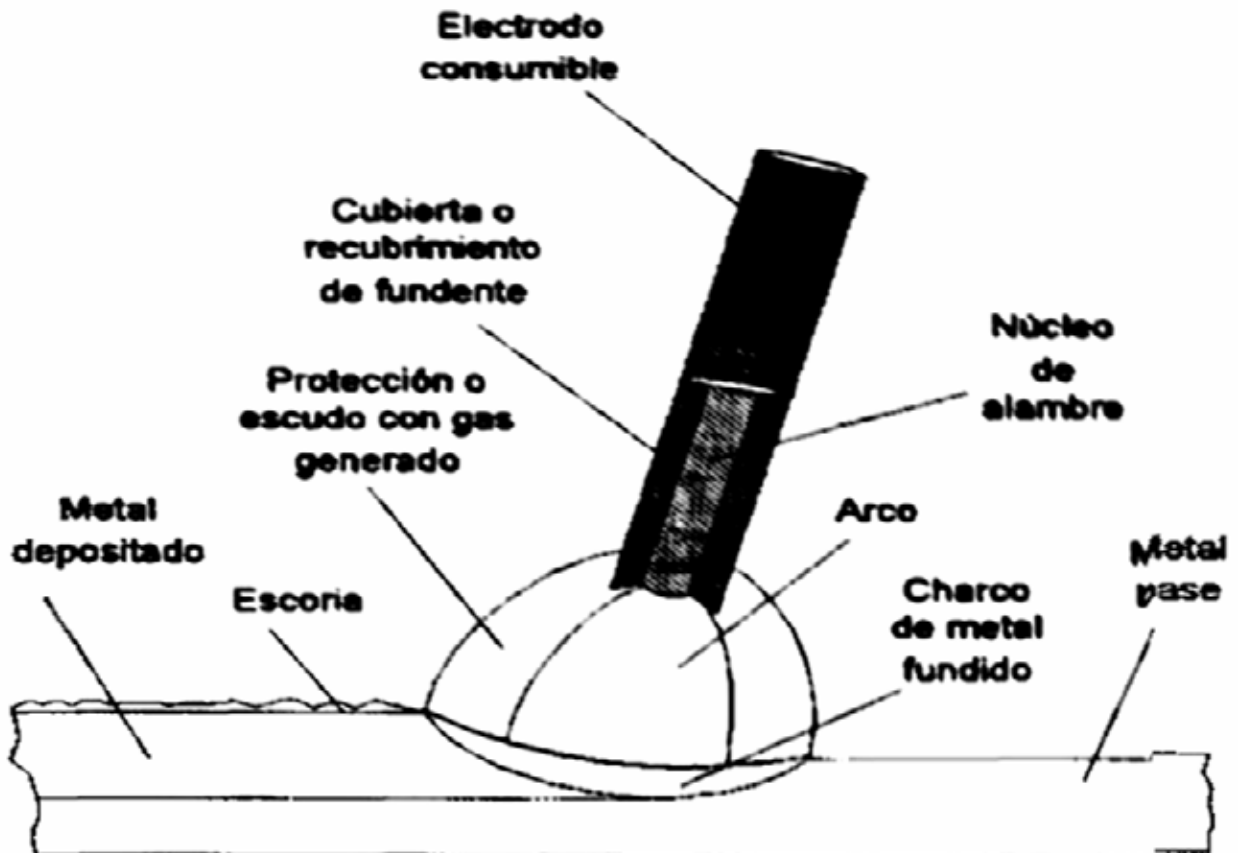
Soldadura de Arco Eléctrico Manual (SMAW)
